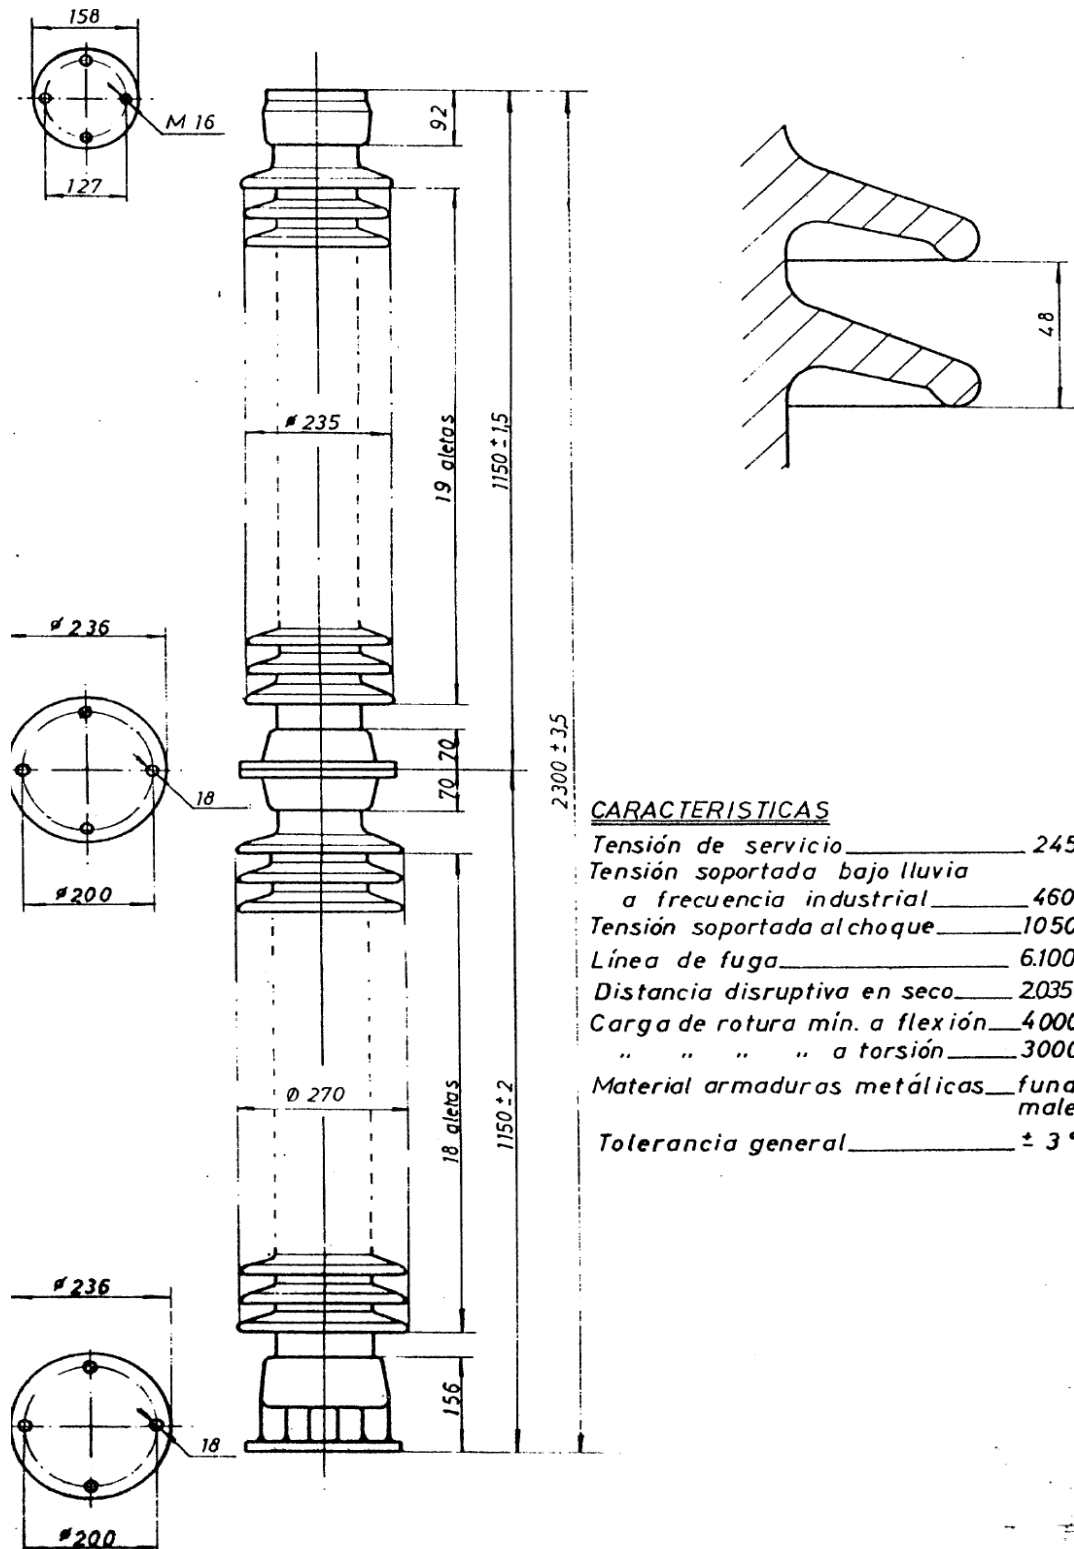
Plano de aislador soporte de cuchillas del seccionador Marca AEG Modelo FMS-414
